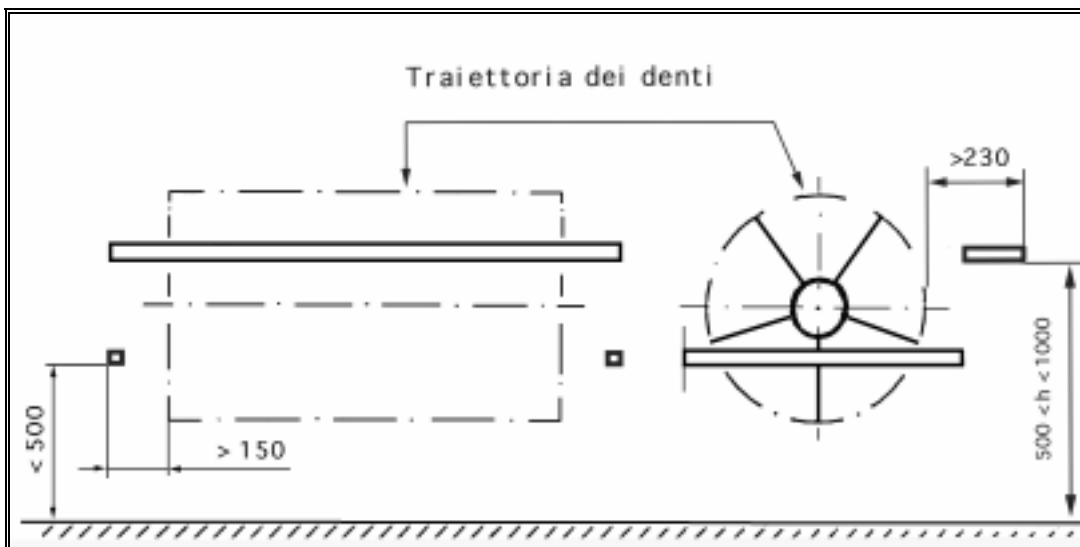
Vista frontale e laterale dei dispositivi di protezione
